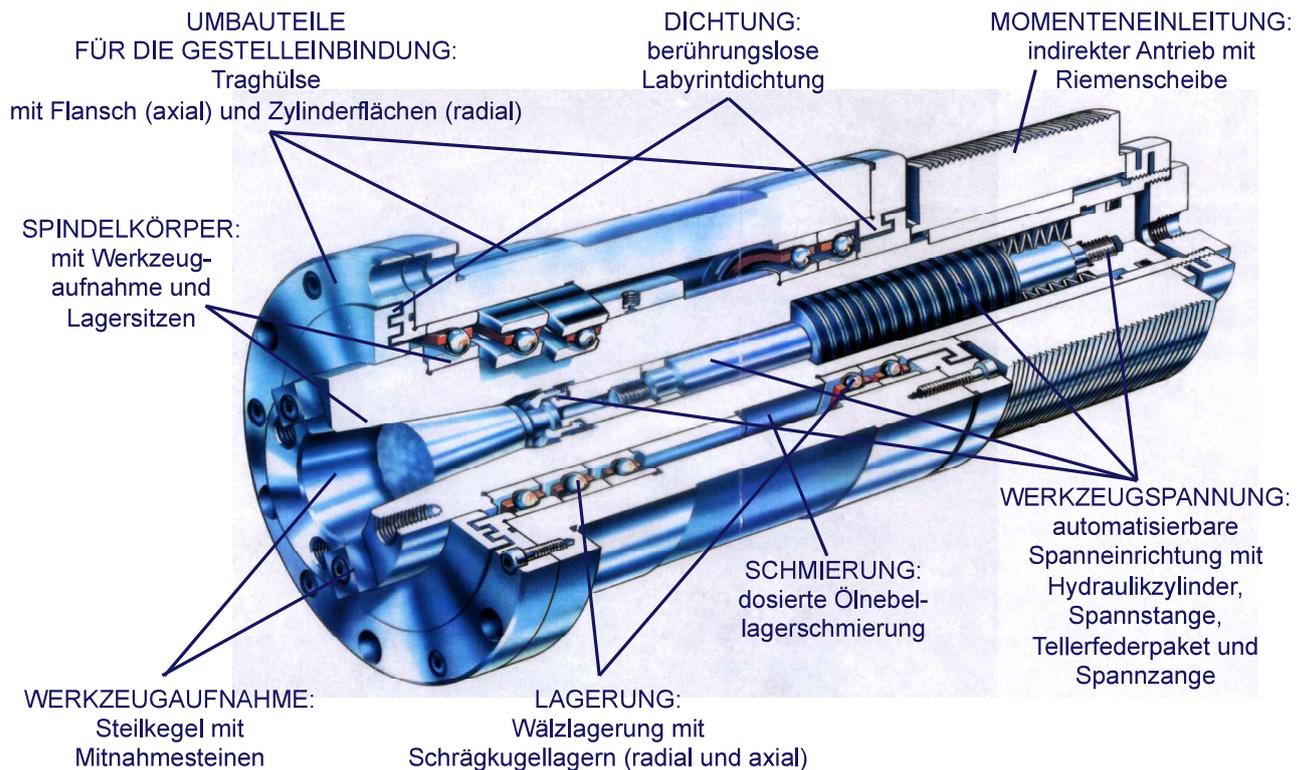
Beispiel einer Arbeitsspindel für eine Fräsmaschine
